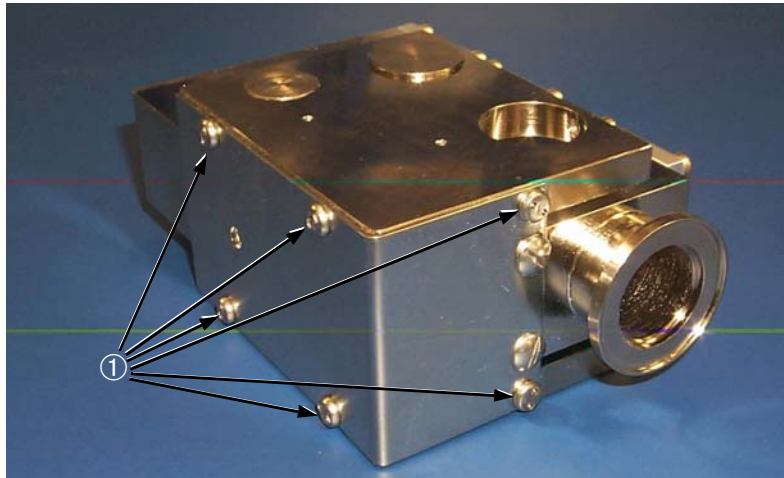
Tornillos de la Abrazadera del Cuerpo del Imán
